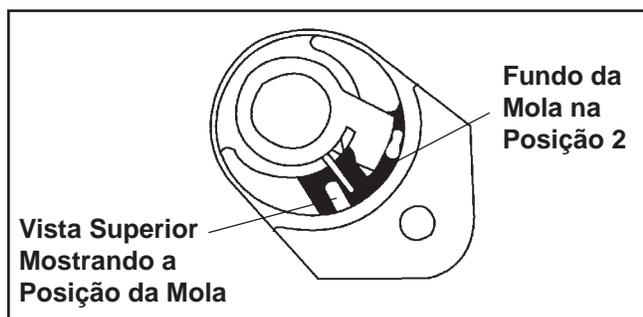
Alavanca do Obturador de Ar com a Tampa Retirada.
